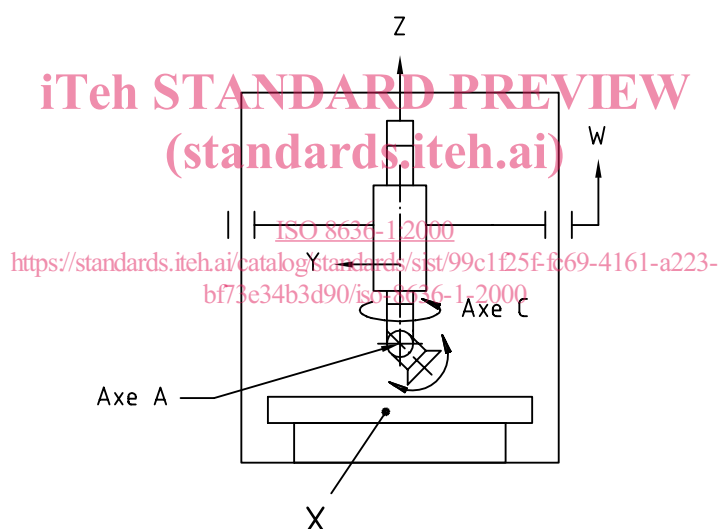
Type 4: Machine à une tête de fraisage sur traverse mobile, avec accessoire de fraisage pivotant selon les axes C et A
